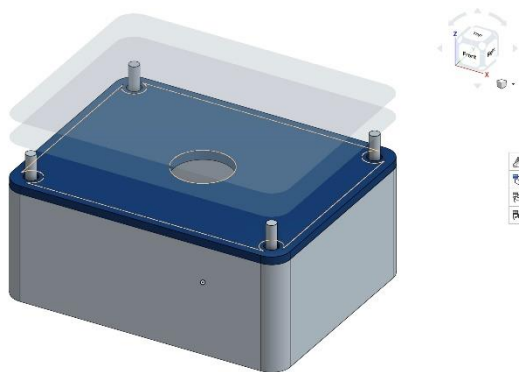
Partie intermédiaire du boîtier: Vue ensemble
